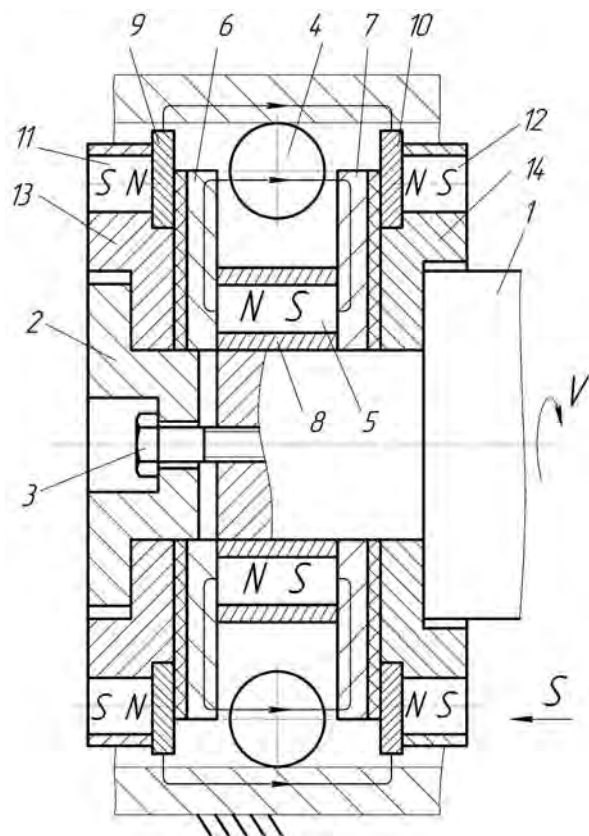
Схема реализации комбинированного магнитно-центробежного накатывания с дополнительным намагничиванием поверхности детали
